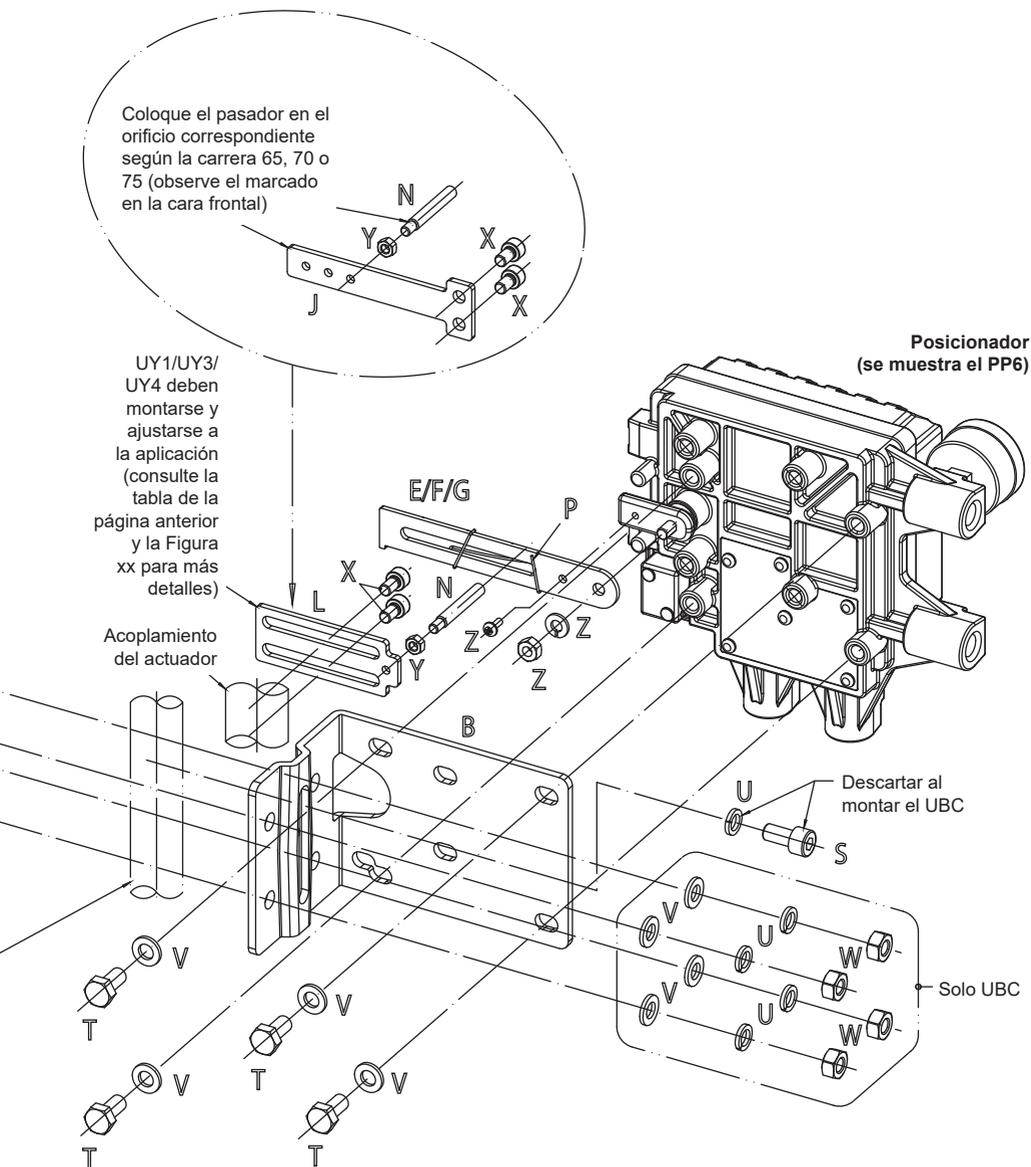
Despiece del conjunto de montaje lateral (se muestra el posicionador PP6)
